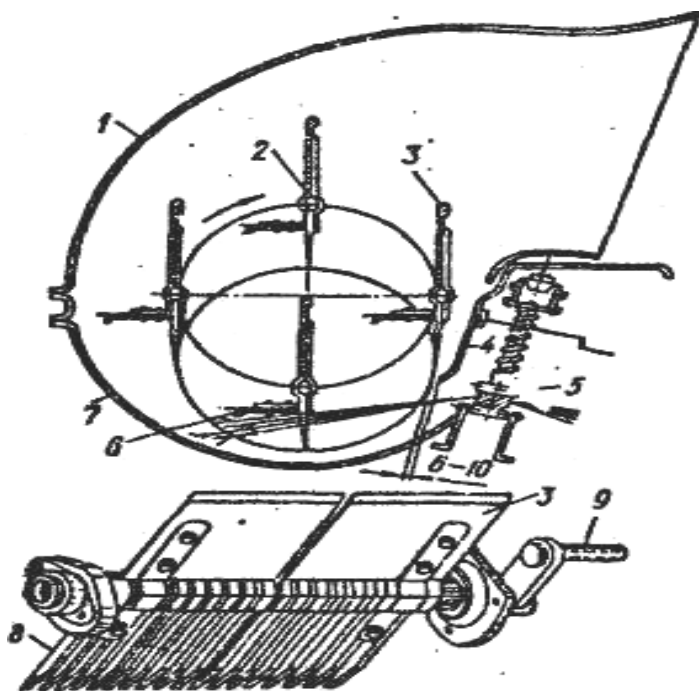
Обчісувальний апарат комбайна ЛК-4А 1 – кожух; 2 – обчісувальний барабан; 3 – вертикальна лопатка; 4 - обмежувальний щиток; 5 – затискний транспортер; 6 – горизонтальна лопатка; 7 – піддон; 8 – гребінка; 9 – кривошип.
